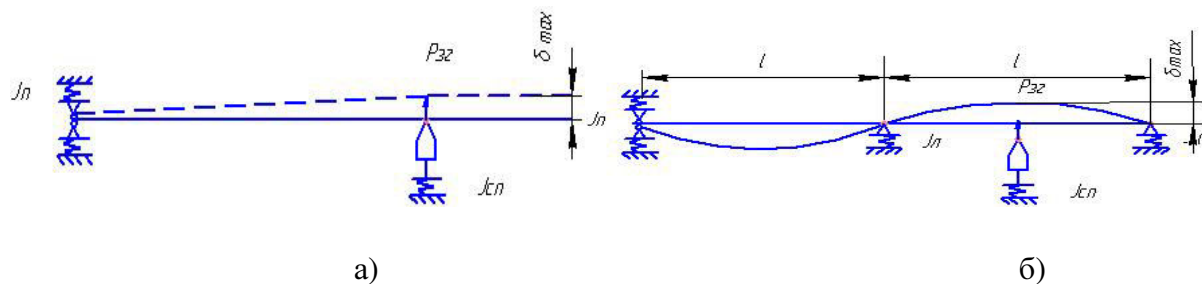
Розрахункові схеми обробки: а) – консольно закріпленої заготовки одним різцем; б) – обробка заготовки, закріпленої в патроні і в центрі одним різцем з люнетом
